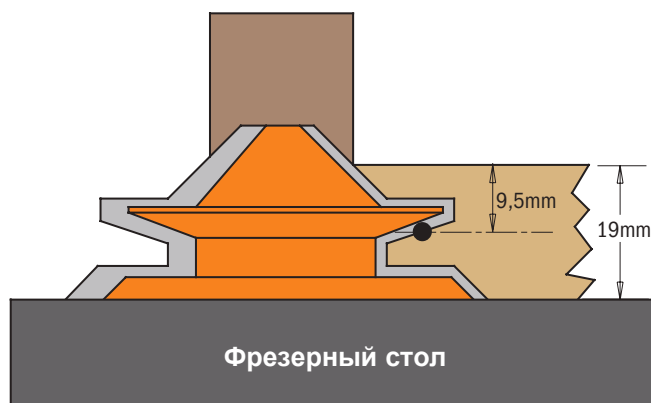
Отфрезеруйте первую деталь внутренней стороной вниз. Убедитесь, что рез проходит через центр детали как на рисунке.
